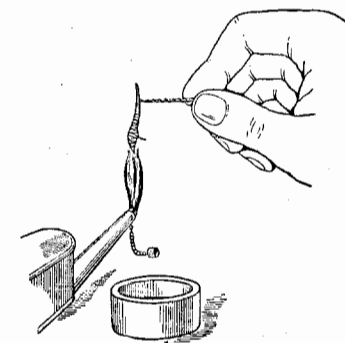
Закалка для крепления пружины во время чистовой обработки (показано стрелкой).
